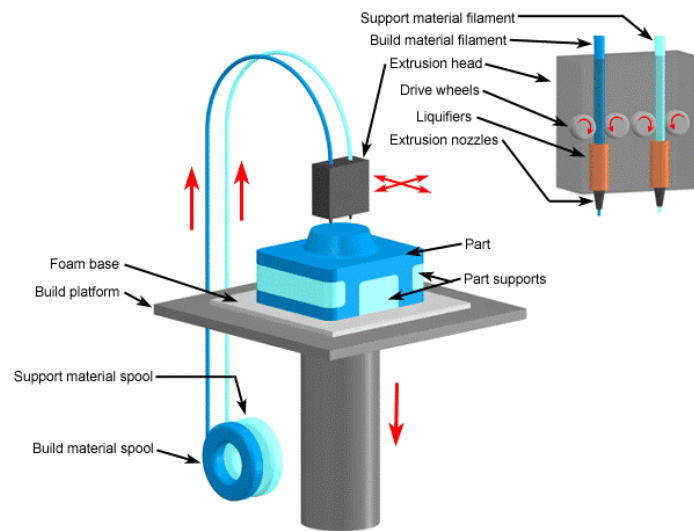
Cabezal de impresión de una máquina FDM.
